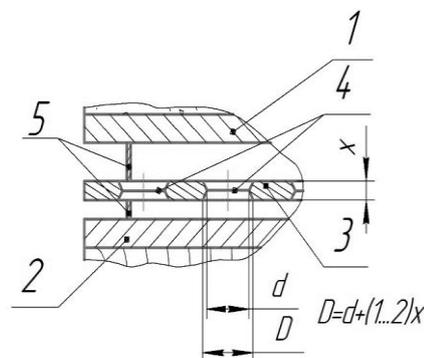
Схема установки армирующих элементов перед сваркой: 1, 2 – пластины из сплава алюминия; 3 – армирующая пластина из титана; 4 – перфорация; 5 – элемент для обеспечения зазора между свариваемыми элементами
